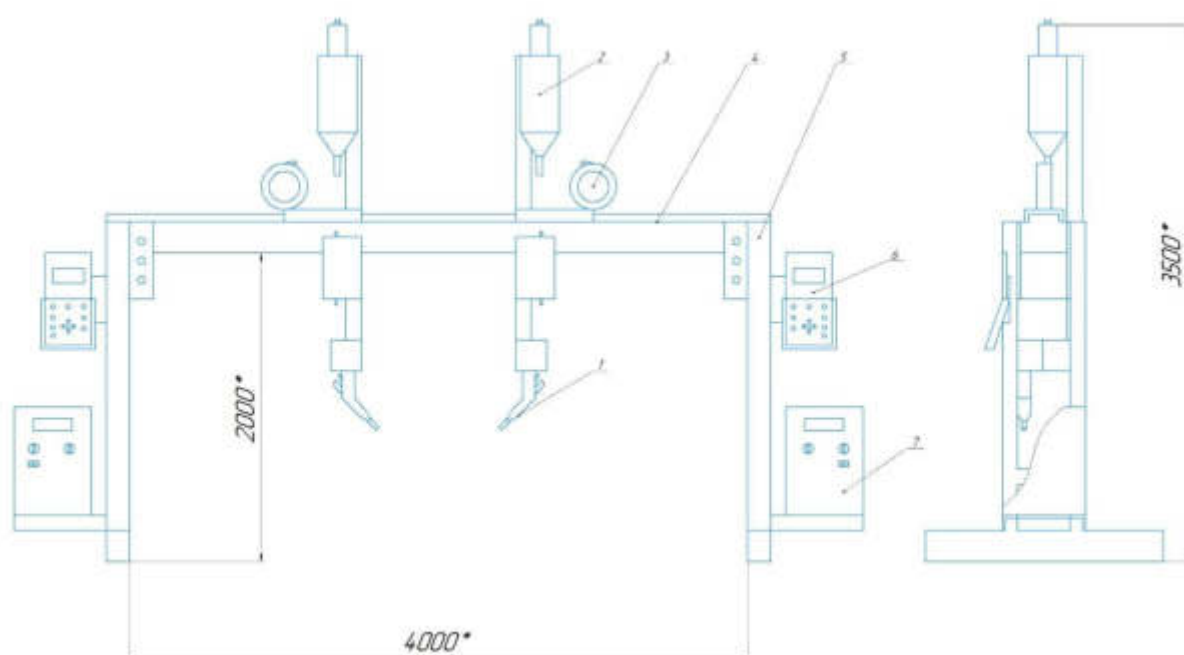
Конструкция сварочного центра портального типа Vebs
